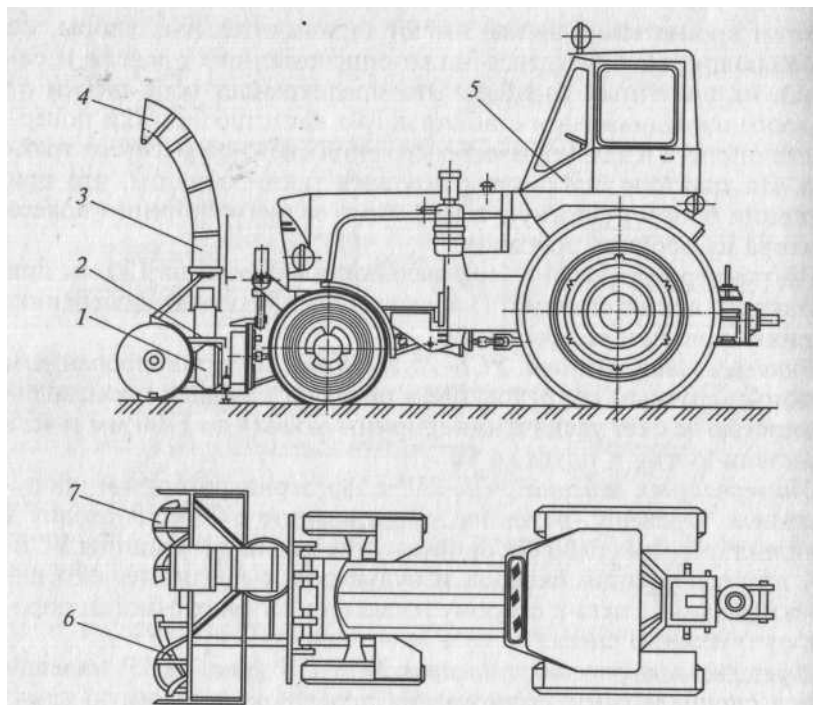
Фрезерно-роторное оборудование УСБ-25Р: 1 — ротор; 2 — рама; 3 — желоб; 4 — козырек; 5 — трактор; 6 — левая фреза; 7 — правая фреза
